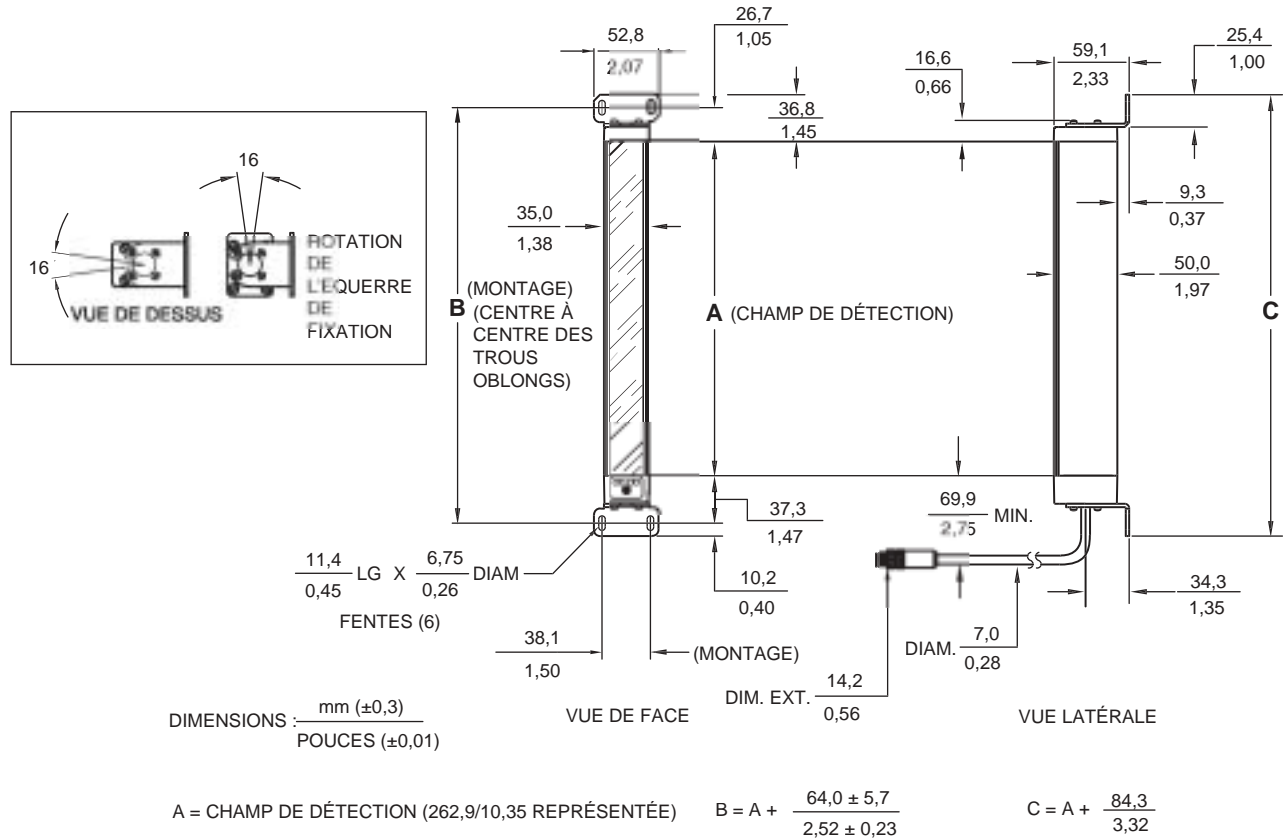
Dimensions (voir le Tableau 18 pour les dimensions A, B et C)
